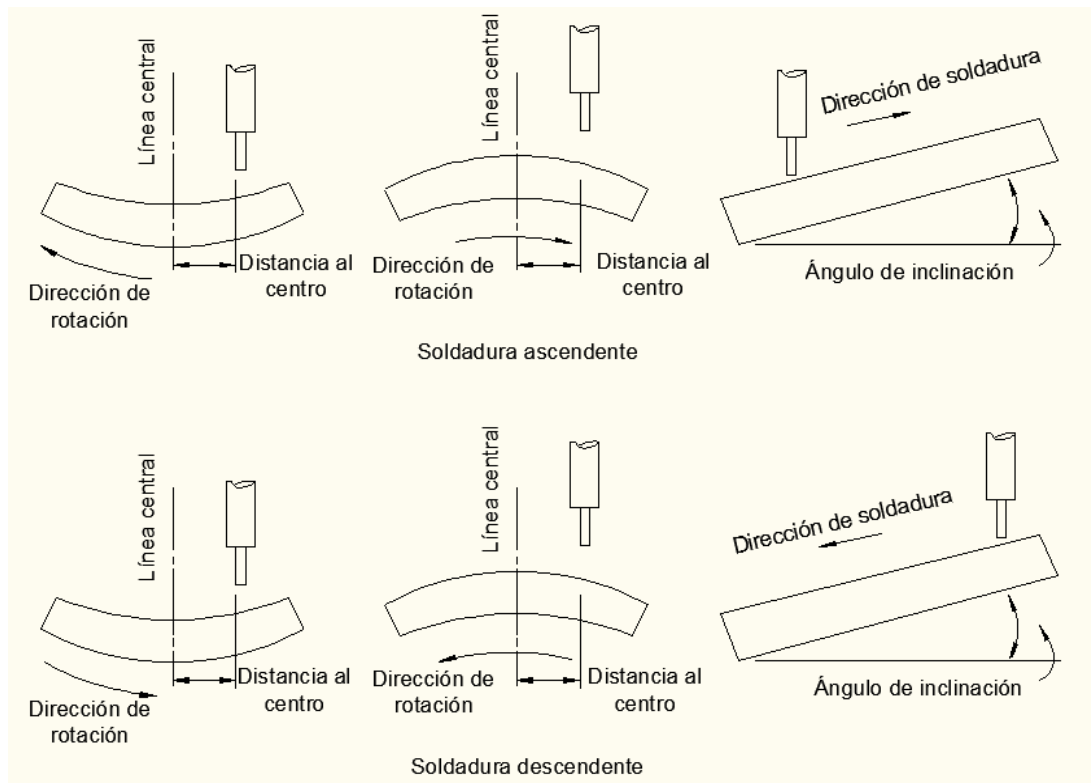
26. Soldadura ascendente y descendente sobre placas y partes cilíndricas [1].
